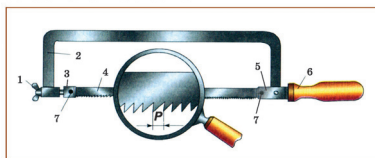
Ручная слесарная ножовка: 1 – натяжная гайка; 2 – рамка; 3 – подвижная головка; 4 – ножовочное полотно; 5 – неподвижная головка; 6 – ручка; 7 – штифты
